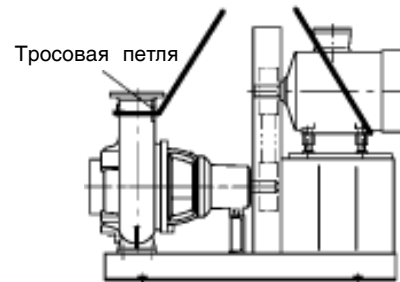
Транспортировка насосного агрегата в сборе (тип установки 3H)
